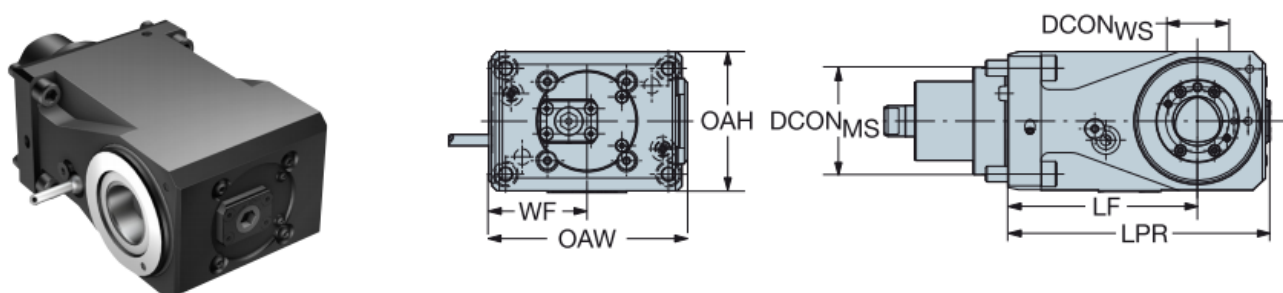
Инструментальные блоки ВМТ-Р для приводного инструмента
